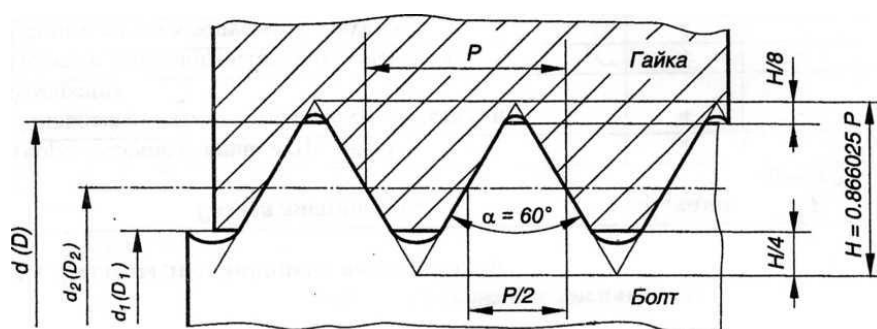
Основные параметры цилиндрической метрической резьбы
